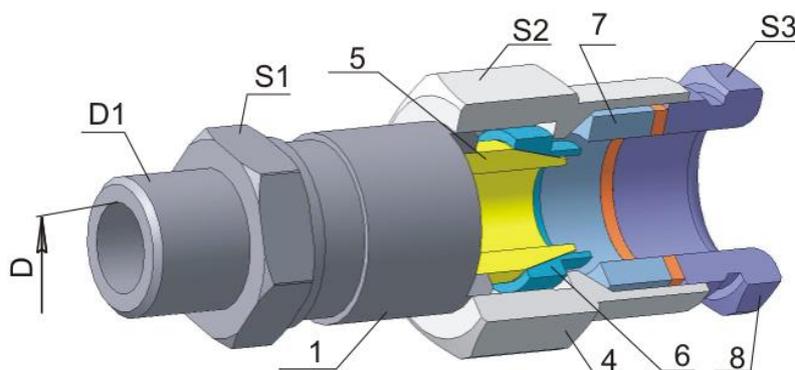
Конструкция кабельного ввода для монтажа бронированного кабеля
